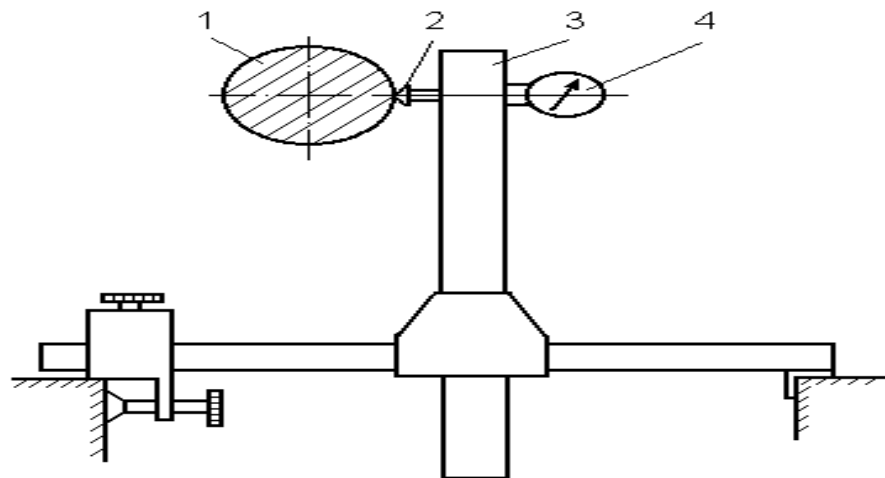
Схема прибора для проверки биения карданного вала:
